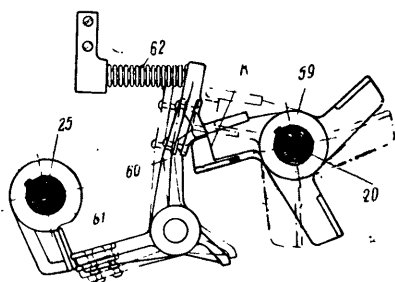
Механическая блокировка между главным и тормозным валами контроллера (блокировка начала торможения):
